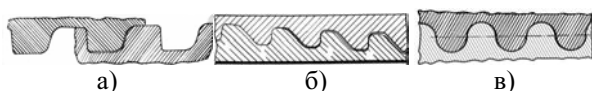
Виды профилей резьбы а – пат. США №3468563; б – пат. США №2909380; в – пат. США №4113290
